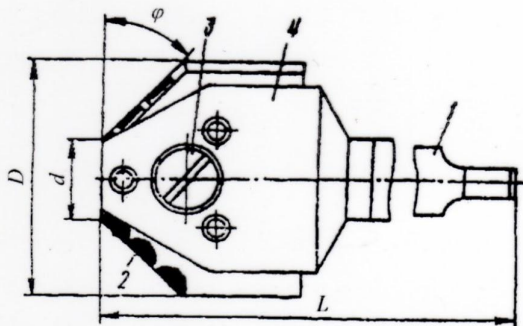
Зенкер, оснащенный режущими элементами из СТМ: 1 – корпус, 2 – сменные многокристалльные ножи, соединенные между собой штифтами 4 и прижатые к корпусу винтом 3.
